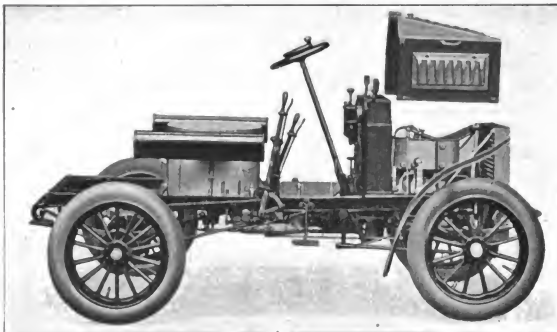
Chassis der White Sewing Mach. Co. in der Ansicht.
